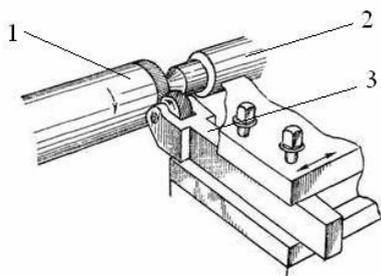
Схема процесса накатки: 1 – деталь; 2 – задняя бабка станка; 3 – державка с накатным роликом
